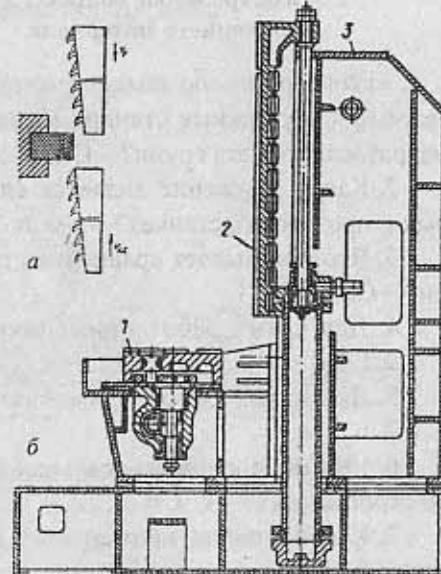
Схема протягивания (а) и общий вид вертикально-протяжного станка (б):
